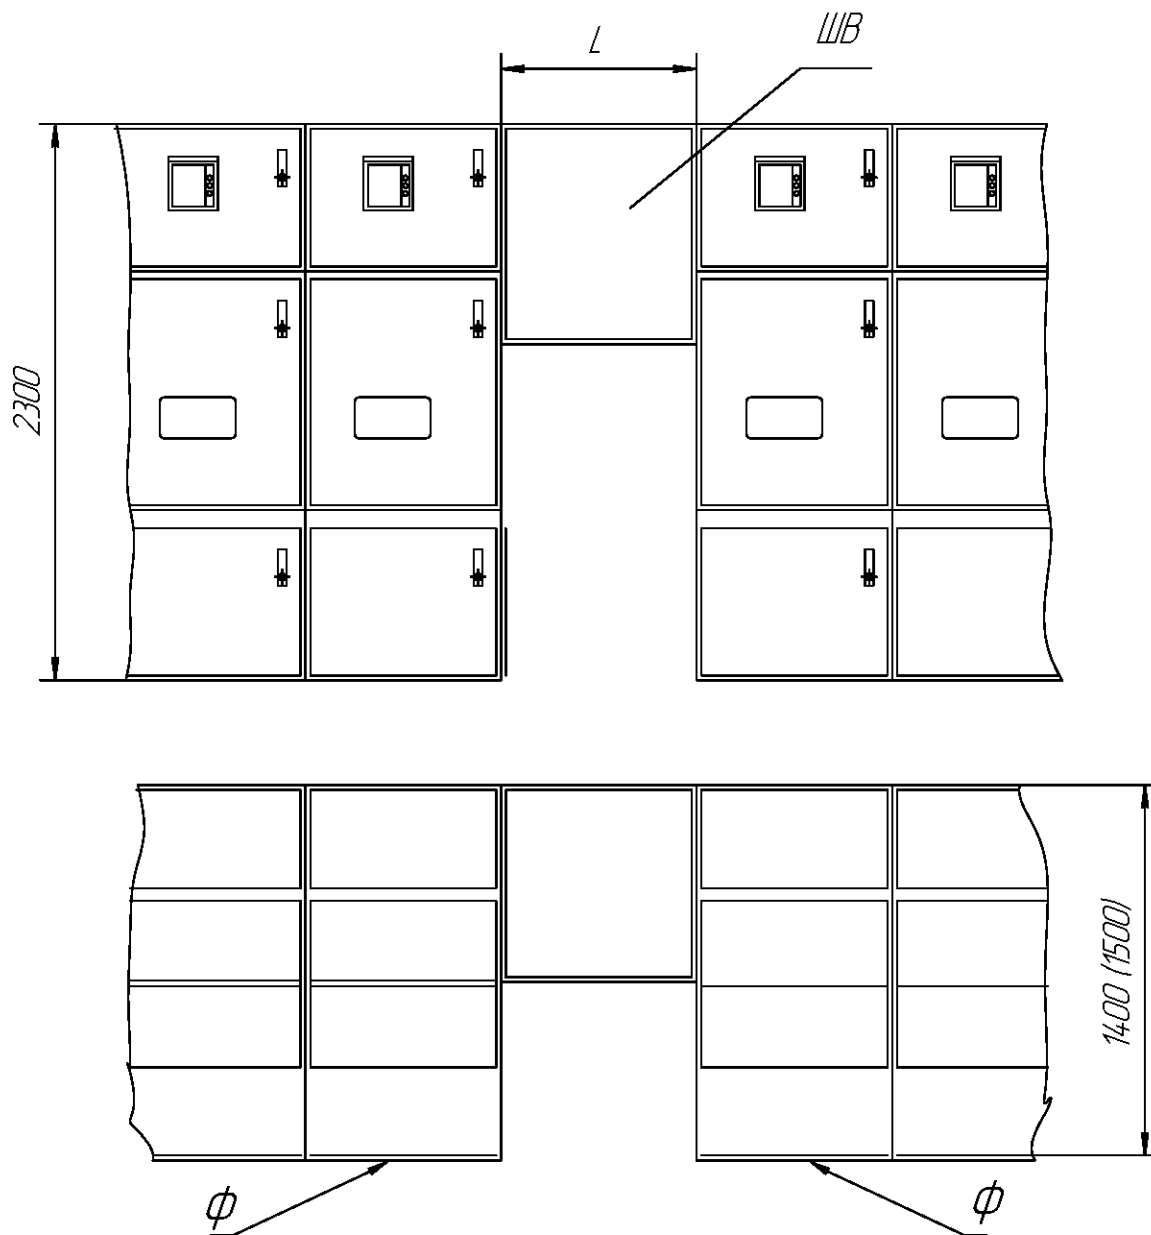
Габаритные, установочные, присоединительные размеры шкафов
